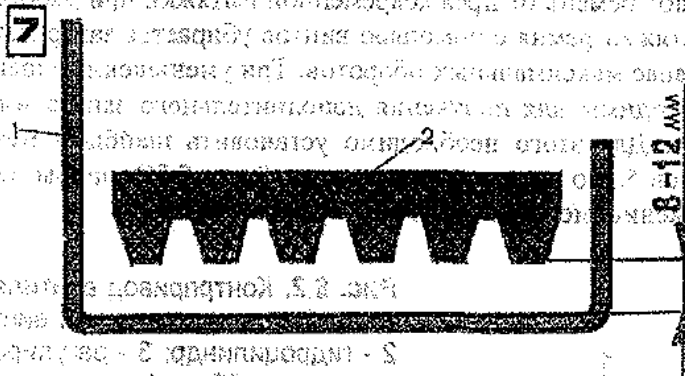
Схема регулировки зазора между верхним кожухом и ремнём: 1 - кожух; 2 - ремень
